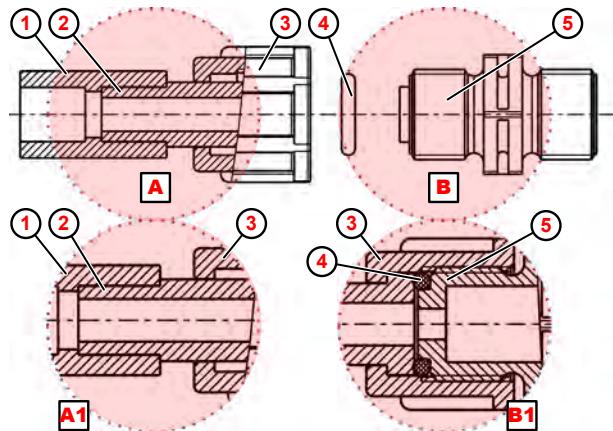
Rohranschluss mit Aufschweißverbindung
